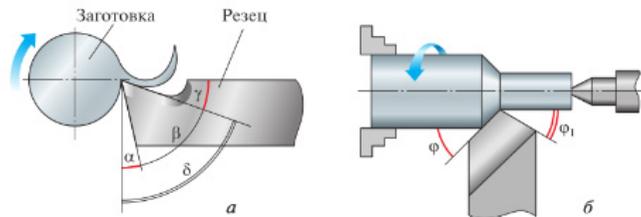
Углы реза: a — основные (α — главный задний; β — заострения; γ — передний; δ — резания); b — углы реза в плане (φ — главный; φ_1 — вспомогательный)
